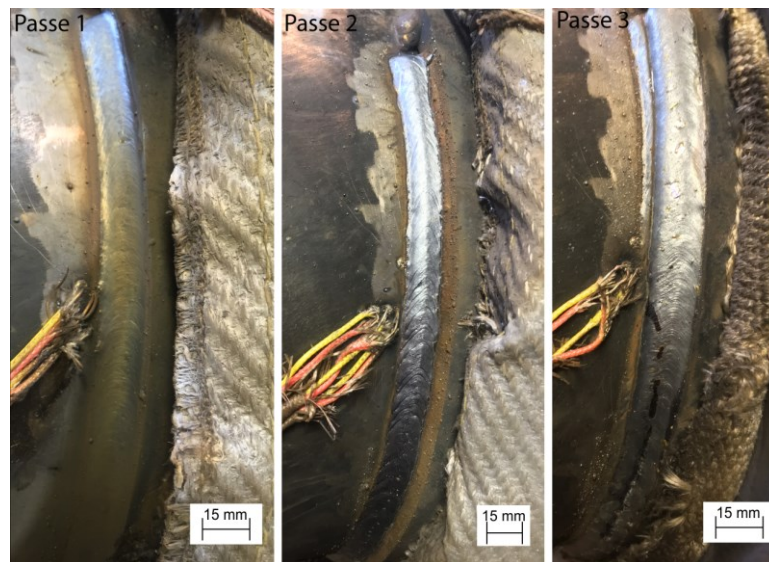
Soldagem orbital de dupla calha tipo-B com GMAW-P DC com pré-aquecimento da calha.
